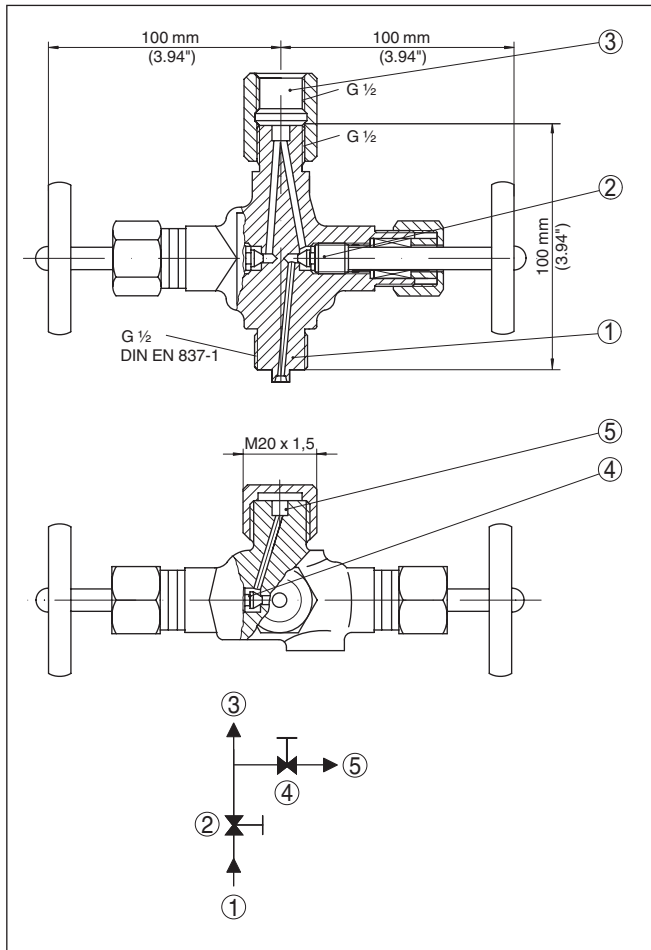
Конструкция двойного запорного вентиля по DIN 16272
